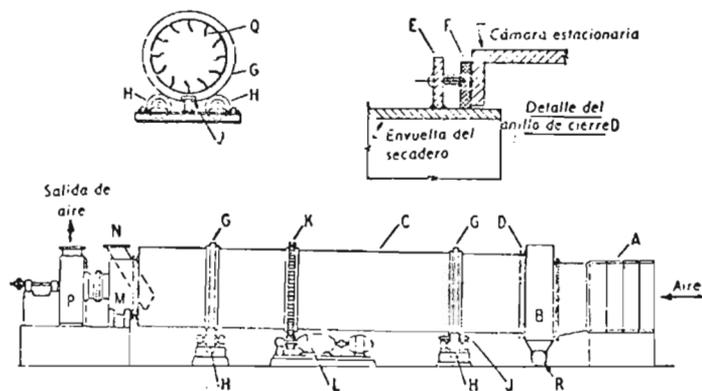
Secador rotatorio. A.- Calentador de aire; B.- cámara estacionaria; C.- envuelta del secador; D.- anillo de cierre; E.- soporte de cierre; F.- anillo de guarnición de cierre; G.- anillos forjados; H.- rodillos soportes; J.- rodillos de empuje; K.- engranaje de movimiento; L.- motor y reductor de velocidad; M.- cámara de descarga de aire; N.- tolva de alimentación; P.- ventilador de descarga; Q.- aletas.
